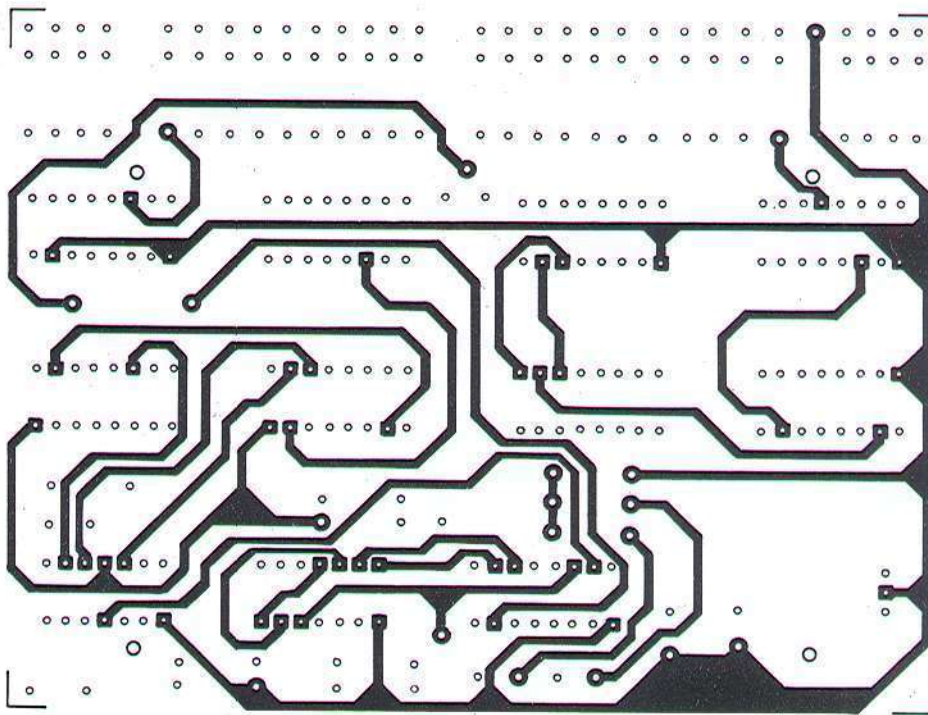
(Cont.) - Montagem em placa de circuito impresso do circuito principal.
